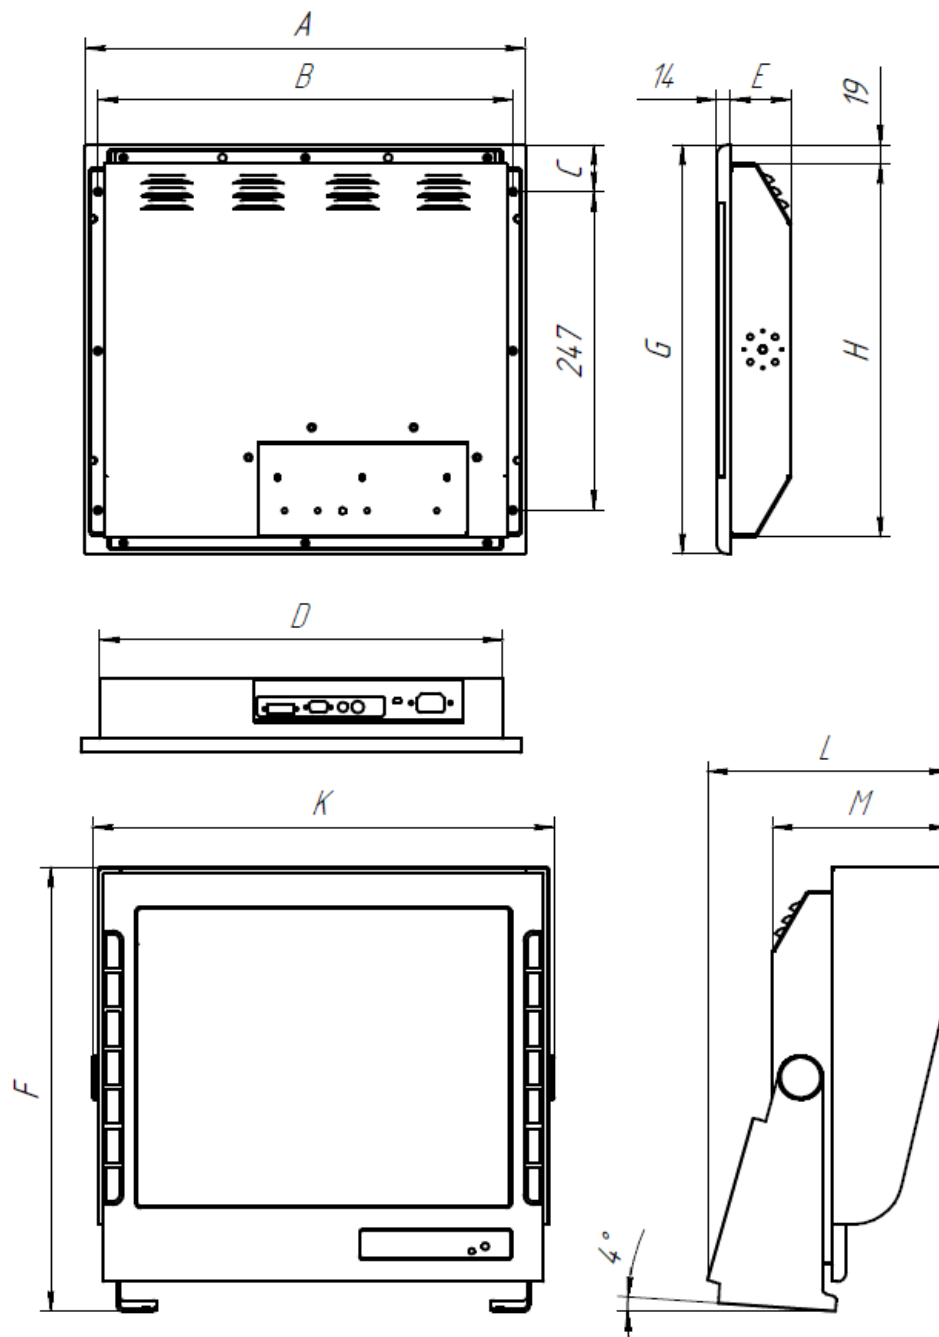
Габаритный чертеж устройства с кронштейном и защитным козырьком
